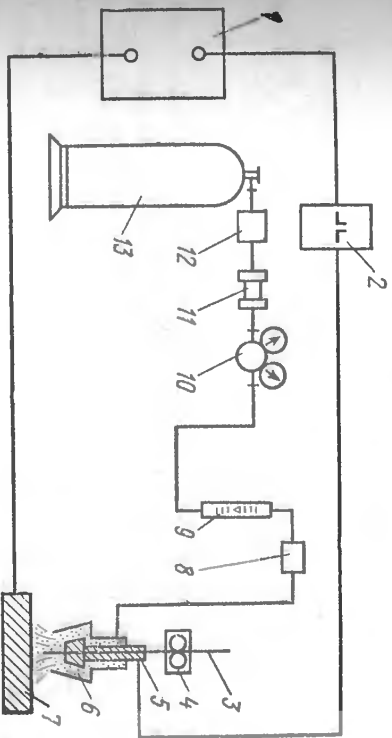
Схема сварки в инертных газах на постоянном токе:
